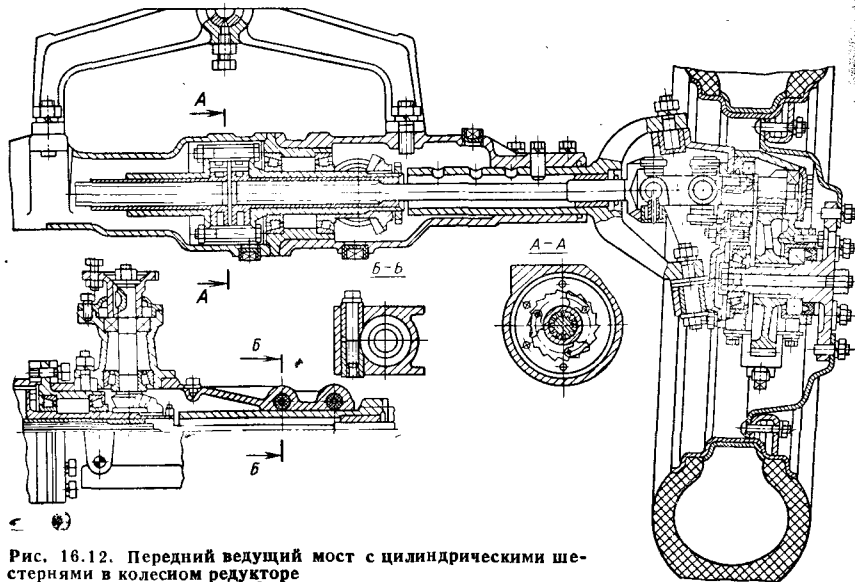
Передний ведущий мост с цилиндрическими шестернями в колесном редукторе
